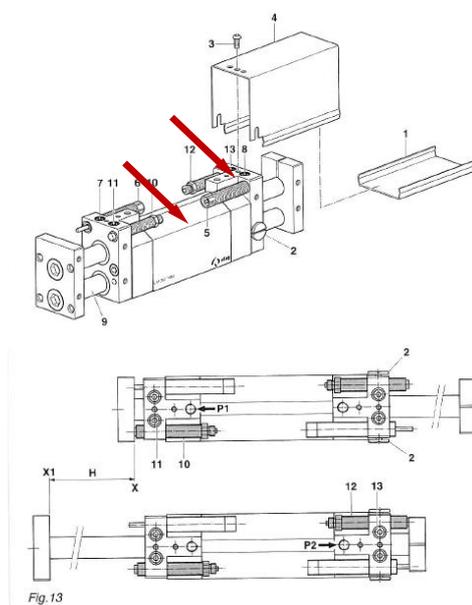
Vis de butée 10 et 12 pour le réglage de la course
